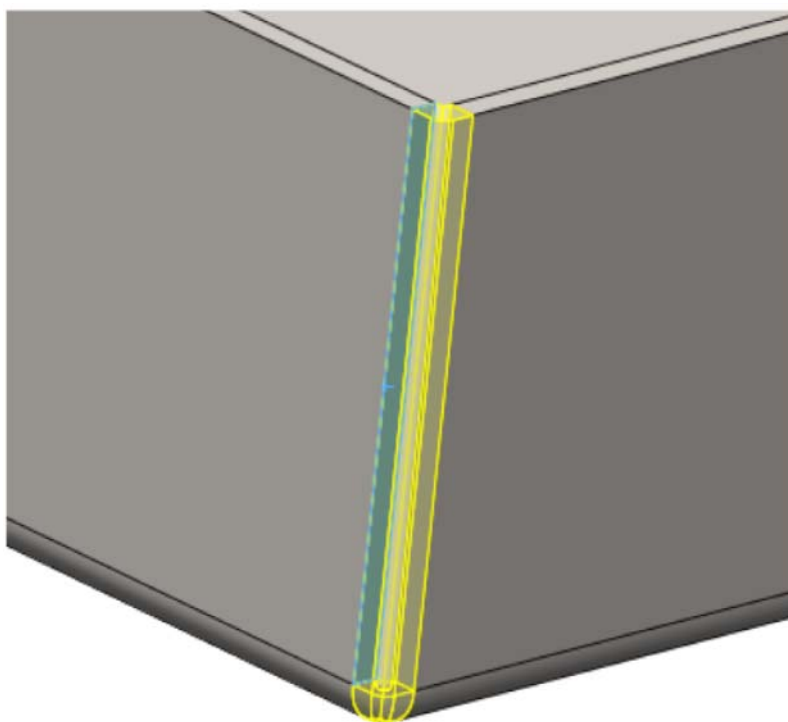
Создание сварного соединения в угловых стыках
